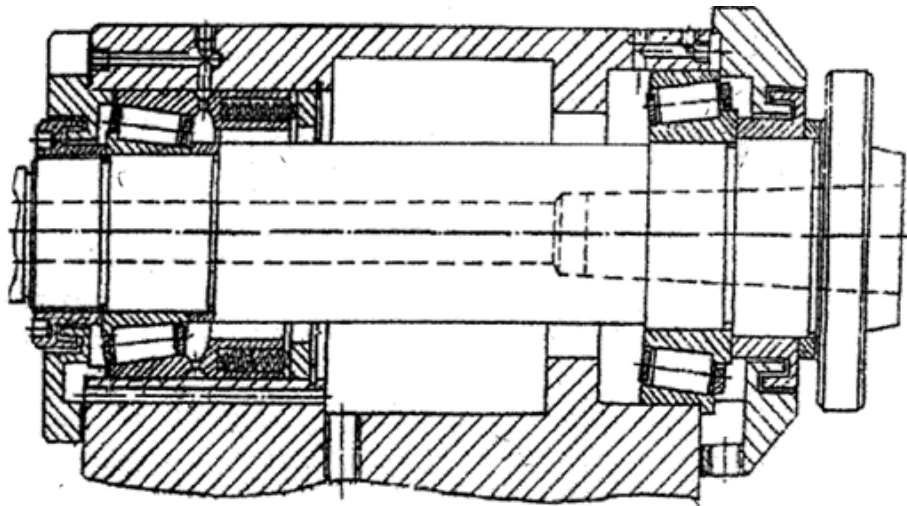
Шпиндельный узел станка с ЧПУ на роликоподшипниках с упорным бортом типа 67000 в передней опоре и типа 17000 в задней опоре
